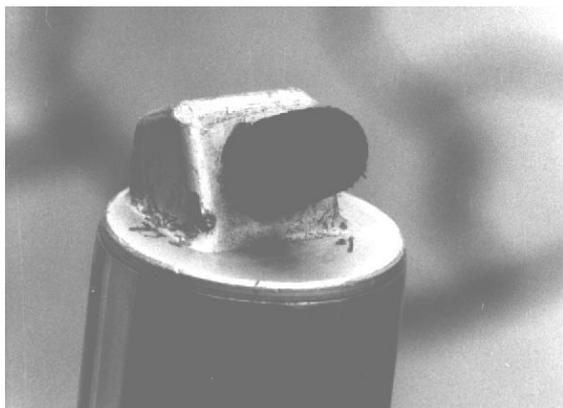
31K ('83-'84): Stopfen zum Schrauben.
